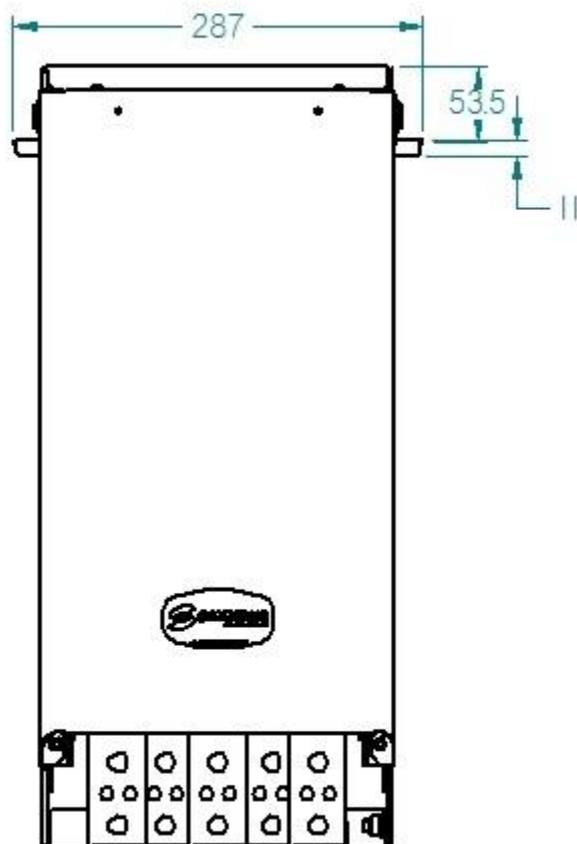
Dimensioni e punti di fissaggio del modulo alimentatore
